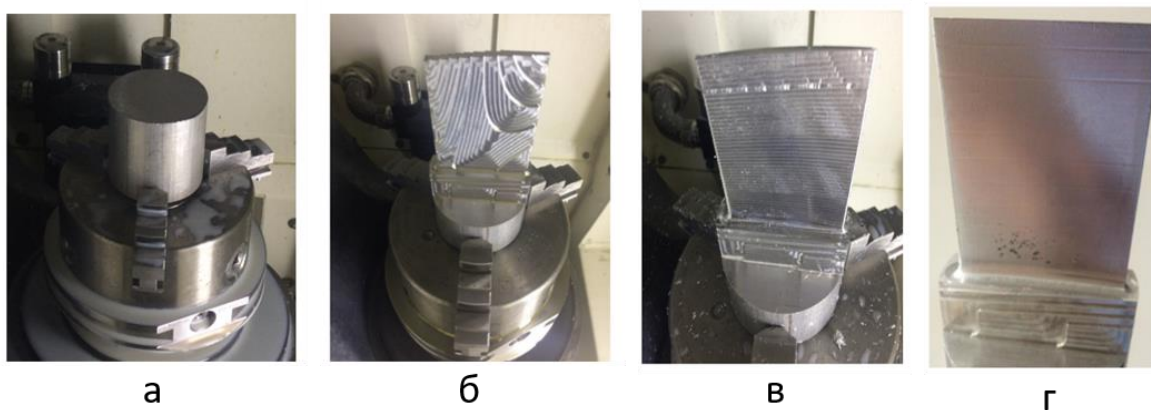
Заготовка на различных стадиях обработки (а – исходная заготовка, б – заготовка после черновой обработки, в – заготовка после получистовой обработки, г – обработанная деталь)
